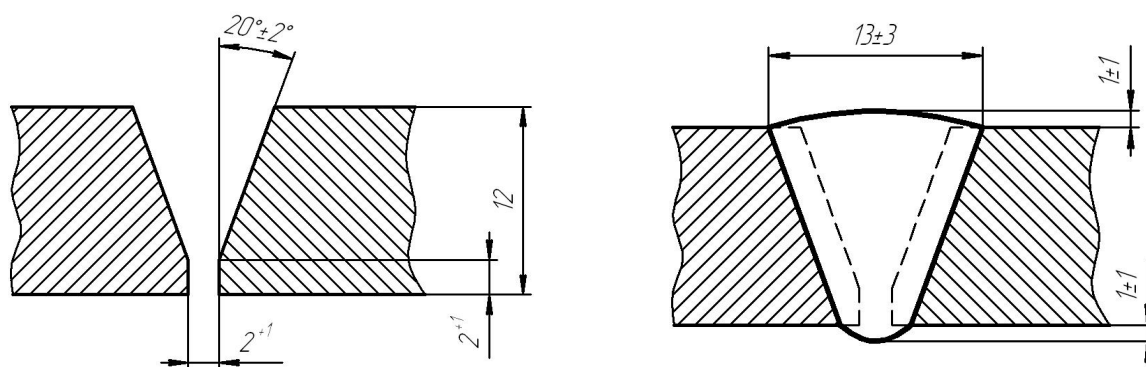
Форма разделки (а) и форма сварного шва (б)
